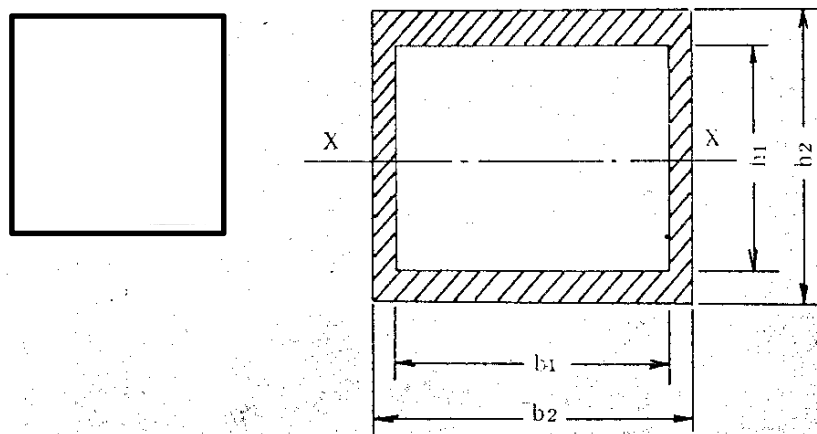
①溶接部の断面 (単位: mm)
